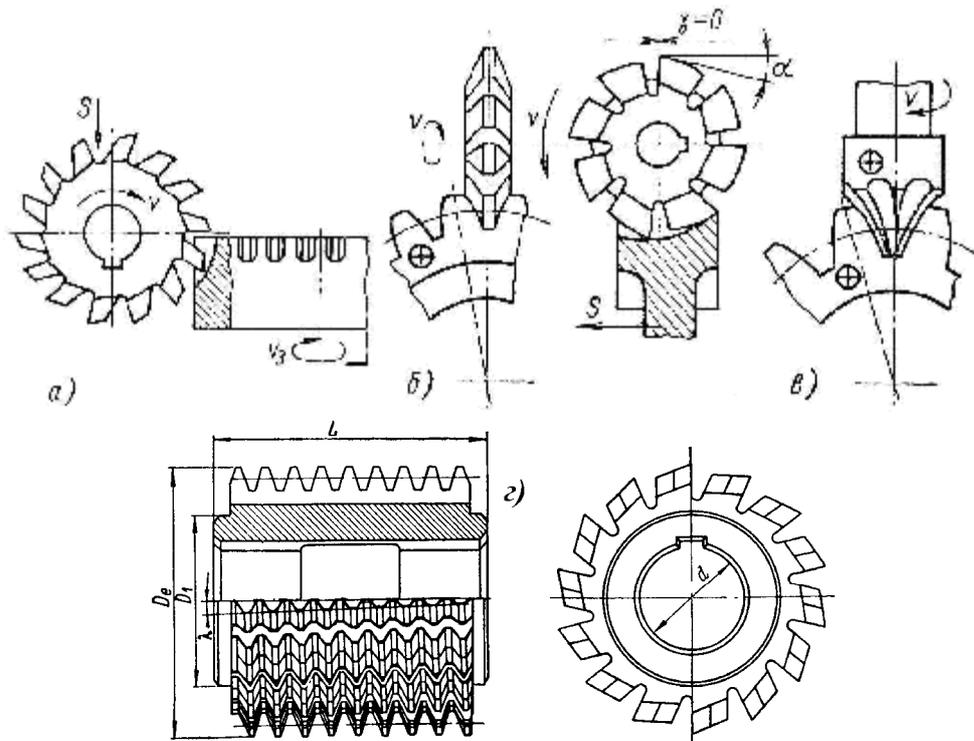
Фрезы для нарезания зубчатых колес методом копирования:
